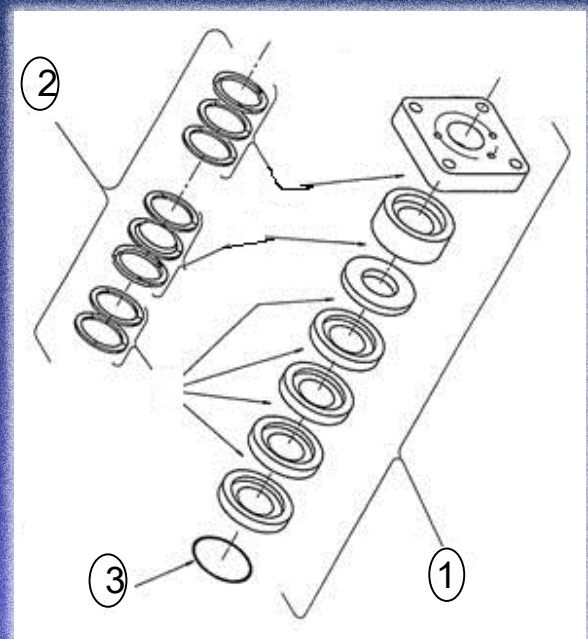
Dibujo mecánico del packing, fuente manual Dresser rand.
